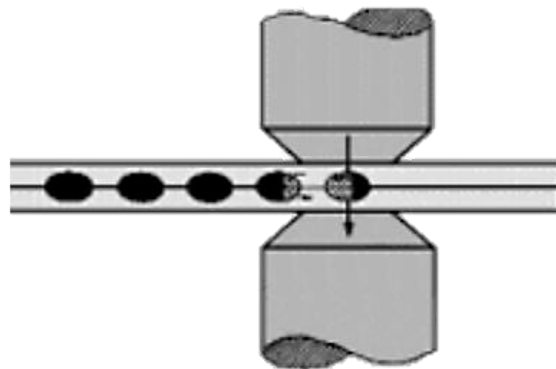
Técnica de soldadura por puntos (EAFNE, 2016).
